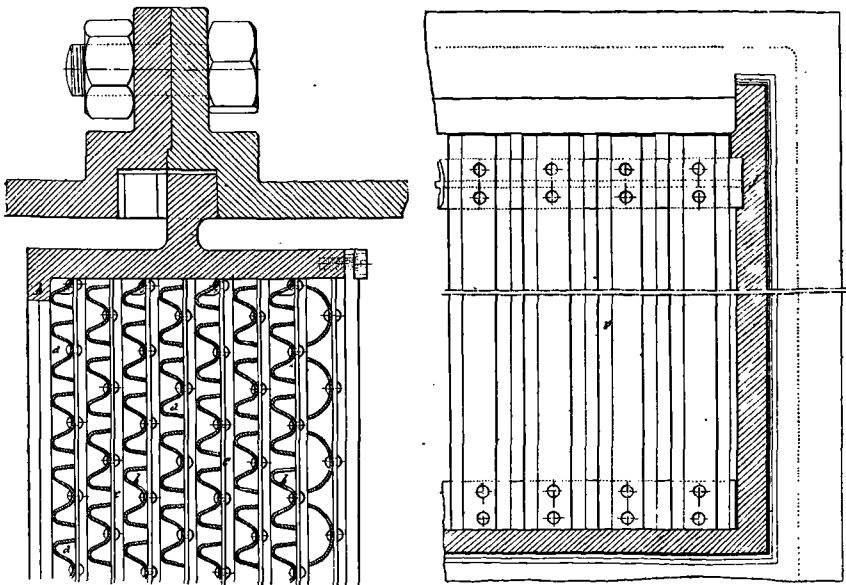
et 222. — Coupe horizontale du plateau et vue de la grille par derrière.
